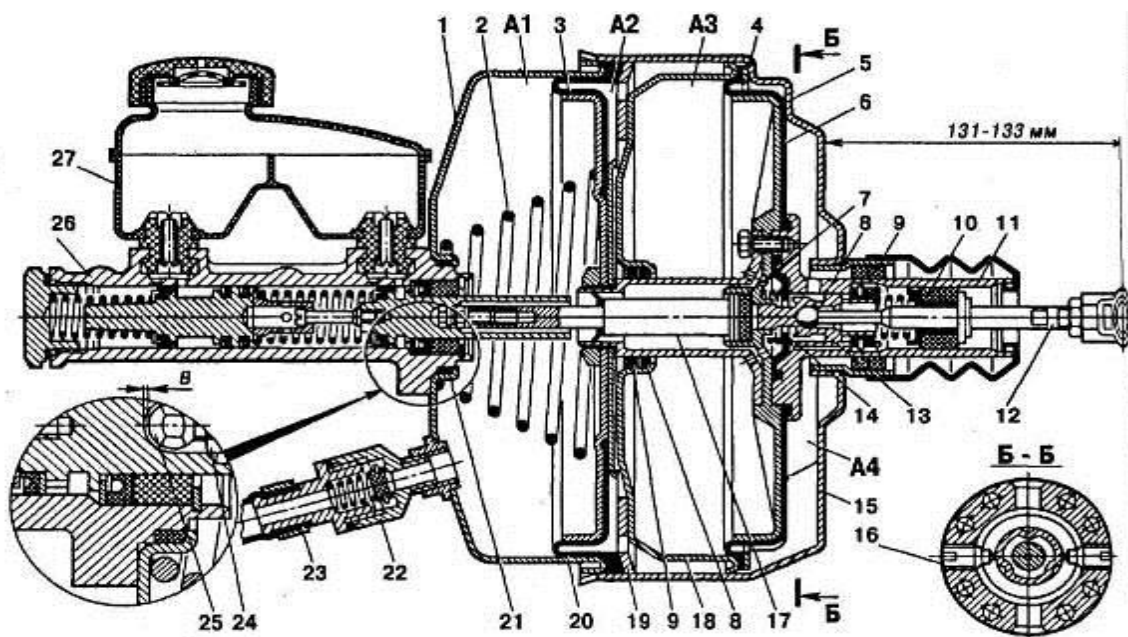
Рабочая тормозная система базового автомобиля ВАЗ-
